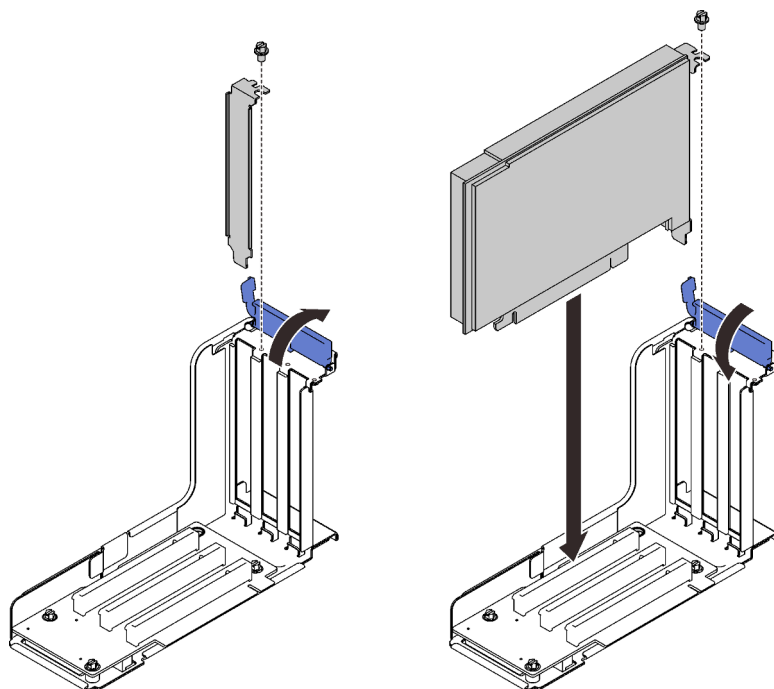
Установка адаптера в блок платы-адаптера Riser PCIe
